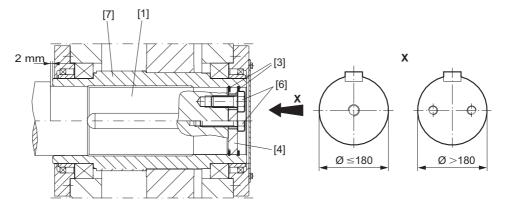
Montaje de reductores horizontales con unión por chaveta
